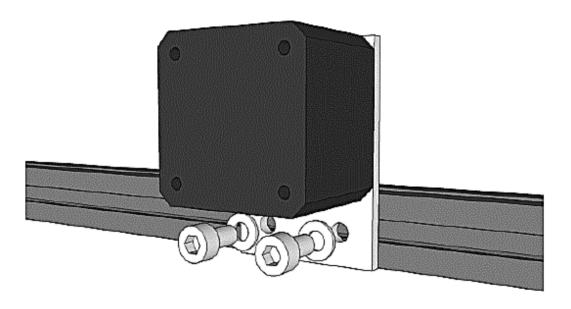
Fijación de motores en perfiles estructurales de aluminio.
